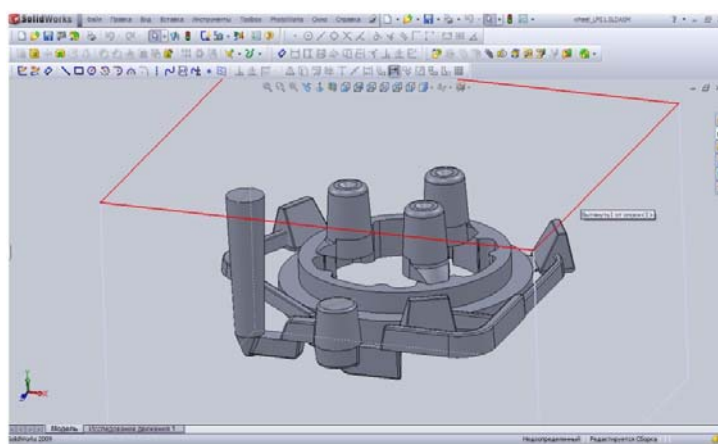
Трёхмерная модель отливки «Колесо»
